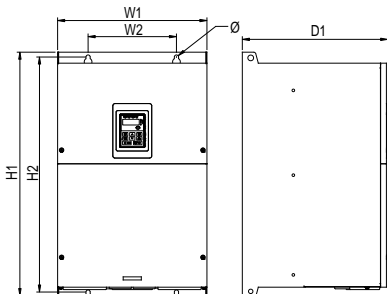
Настенный монтаж ПЧ 3ф 380 В (90-110 кВт)
